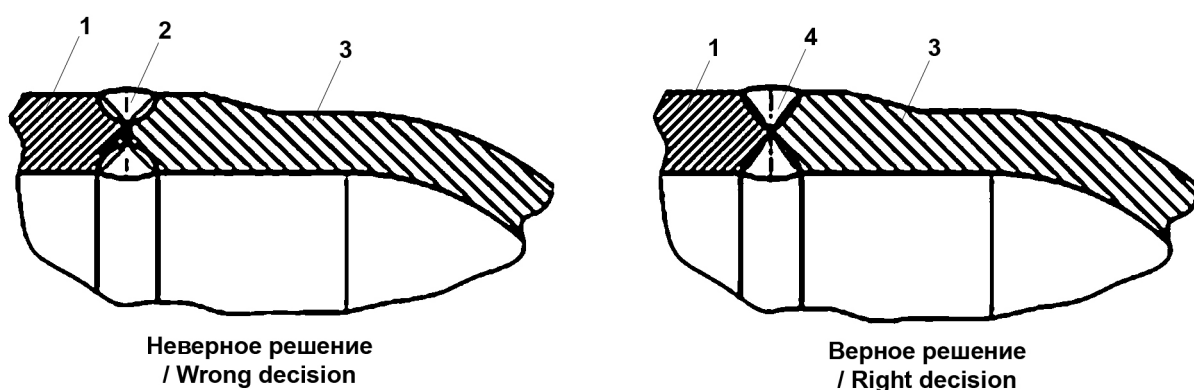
Верное и неверное решения при выборе конструкции сварного кольцевого шва: 1 – обечайка; 2 – наплавленный металл шва; 3 – конструктивный непровар; 4 – днище. I – кольцевой шов, имеющий конструктивный непровар; II – кольцевой шов без конструктивного непровара
